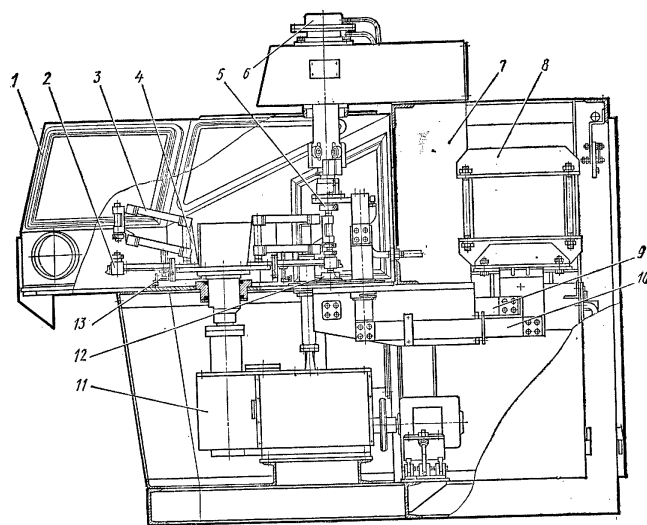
Конденсаторная машина типа МРК-2001 для рельефной сварки корпусов полупроводниковых приборов
